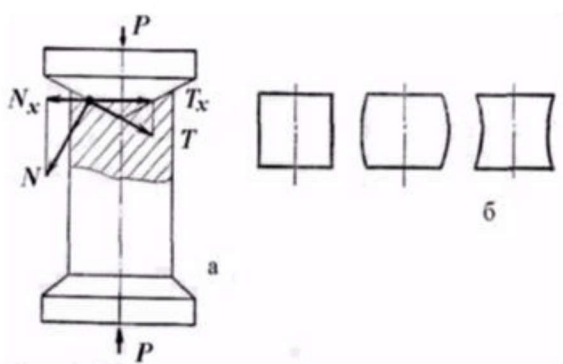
Осадка заготовок: *a* – коническими плитами; *б* – форма боковой поверхности образцов [13]
